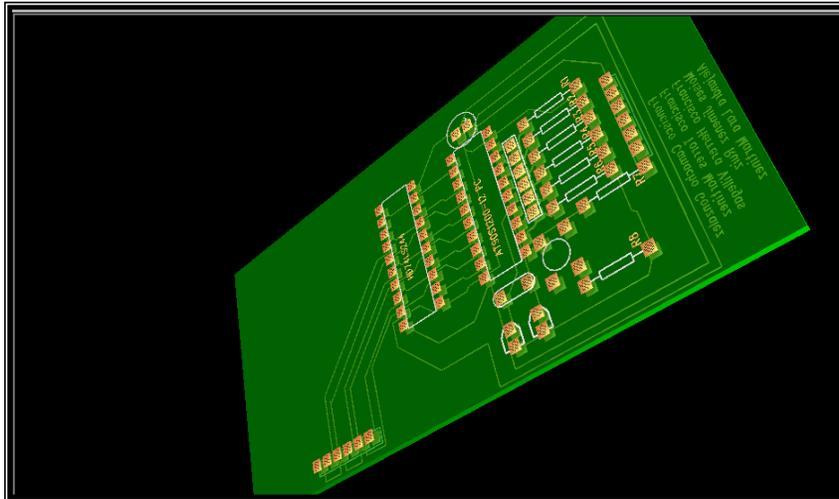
Tablilla perforada lista para colocar y soldar los componentes.
